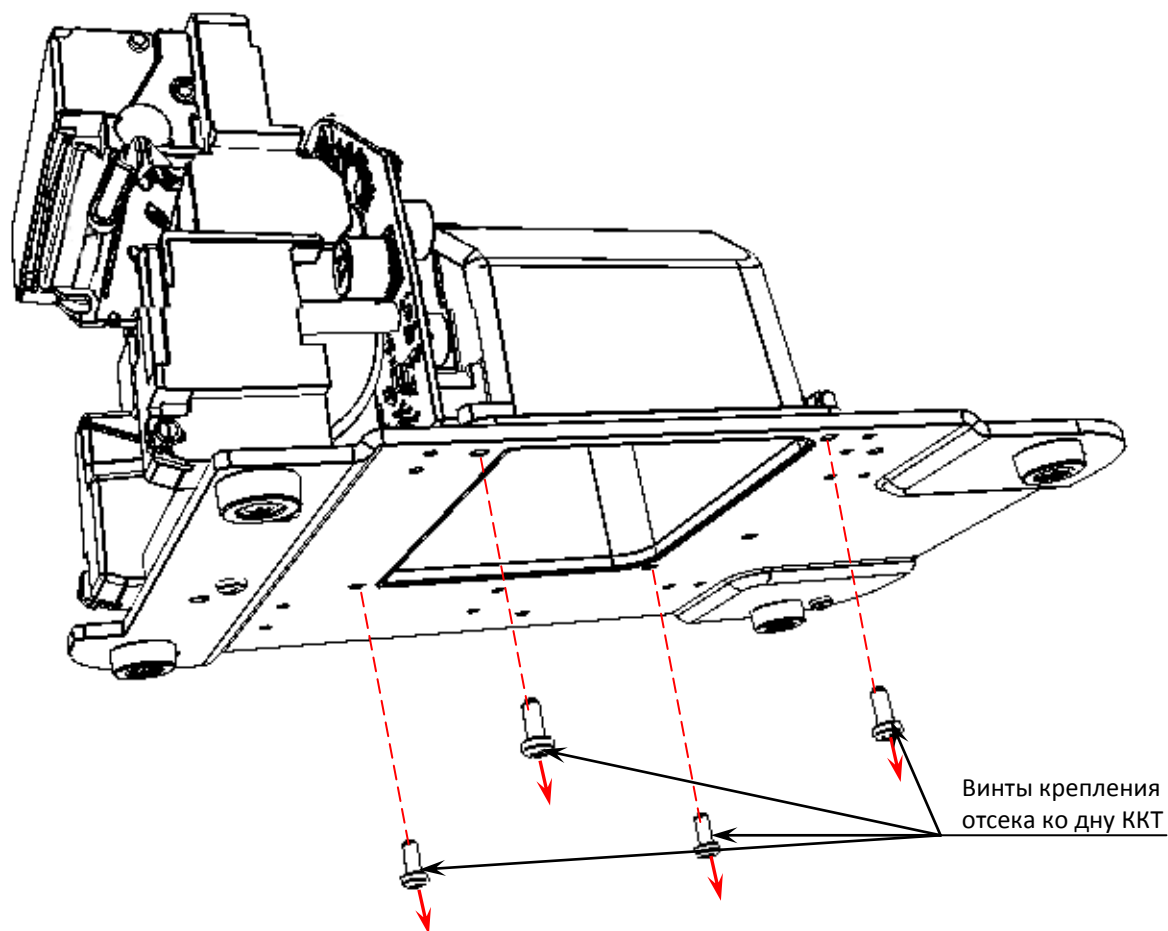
Винты крепления отсека ко дну корпуса ККТ (крышка лотка для ЧЛ не показана)
